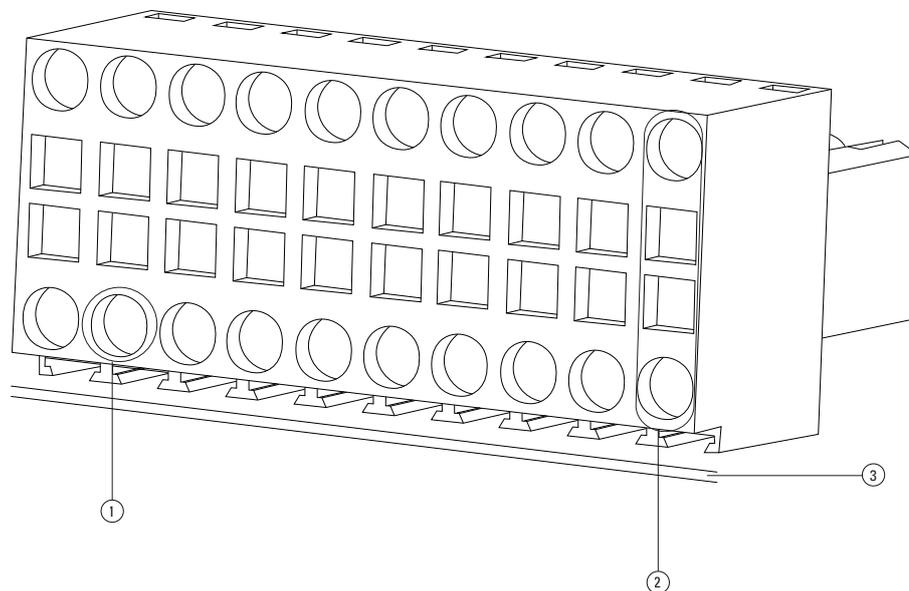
Draufsicht auf die Position des Steckers J9 auf der AC-Plattform
